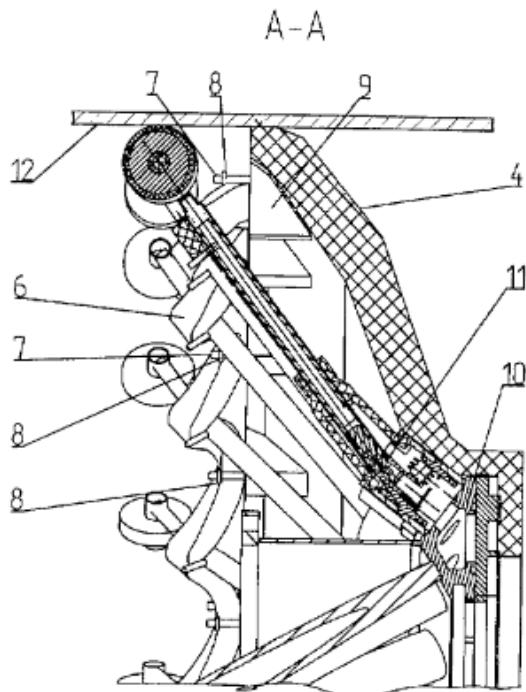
Разрез А-А по оси измерительного рычага внутритрубного профилемера
